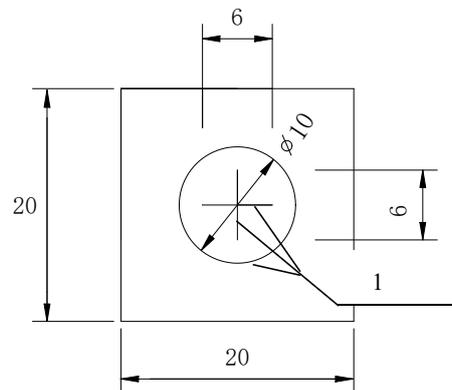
11 A 型灵敏度试片的尺寸 (mm)
